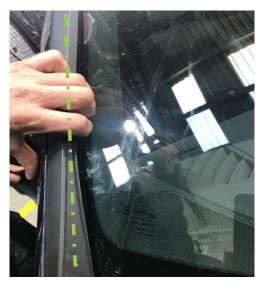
Recorrido del cable del módulo por la moldura exterior del marco del parabrisas
